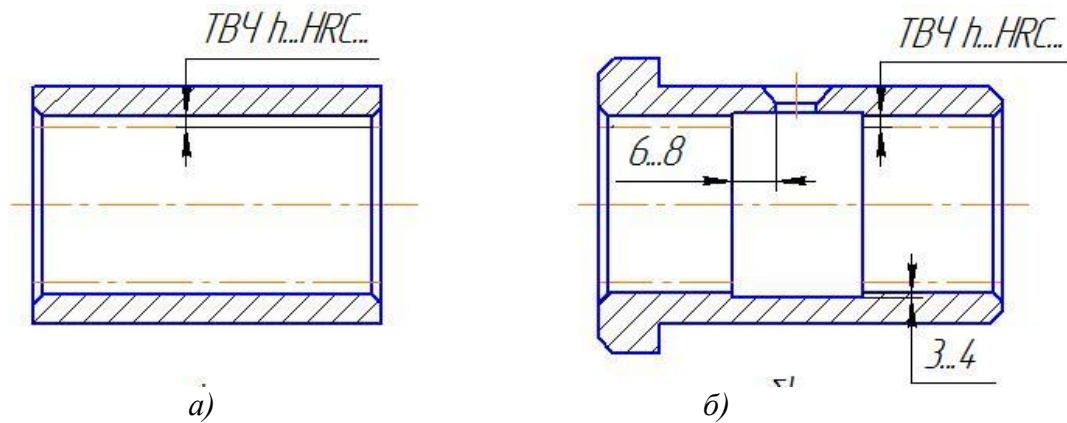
Обмеження щодо призначення загартування деталей
